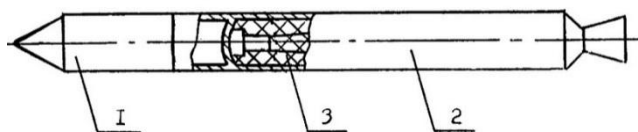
Устройство самоликвидации ракеты с твердотопливным двигателем RU 2111447С1
